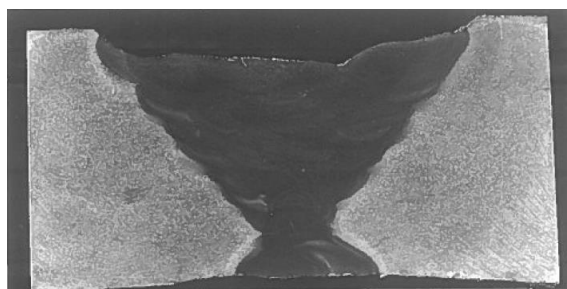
coupe d'une soudure sur EN-GJS 500-14
